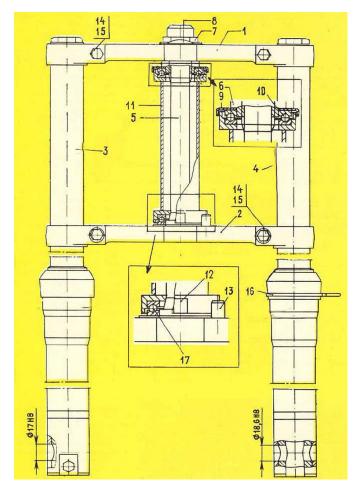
Horquilla anterior: 1-puente superior; 2-puente inferior; 3-barra derecha de la horquilla; 4-barra izquierda de la horquilla; 5-eje de la columna de dirección; 6- el casquillo de rodamientos; 7-tapón; 8-arandela de seguridad; 9-anillo protector; 10-cojinete superior 778707; 11-marco de la motocicleta, pipa; 12-tope; 13-limitador del tope de la horquilla (solo se muestra uno); 14-bulón; 15-arandela; 16-soporte del cable del freno; 17-cojinete inferior 778707.
